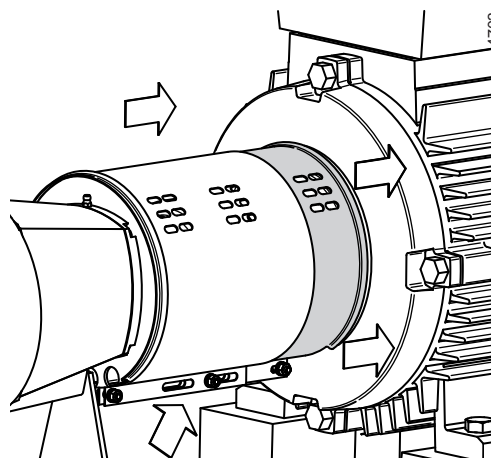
Einstellen des Mantels auf der Motorseite.
